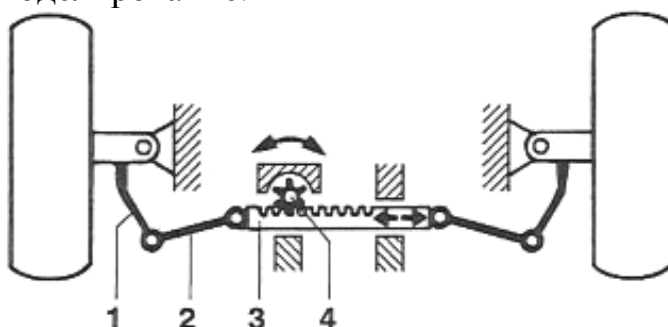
Стандартная схема рулевого реечного управления: 1 – рычаг поворотного кулака, 2 – рулевая тяга, 3 – рулевая рейка, 4 – шестерня
